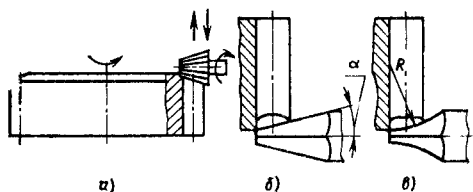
Схема обработки торцовых поверхностей зубьев пальцевыми фрезами:
